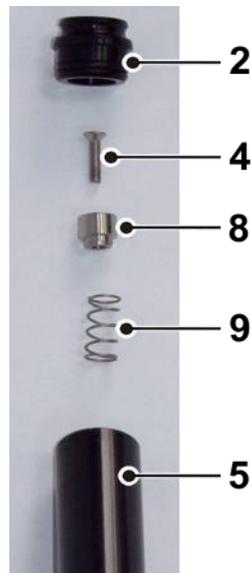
Rotoraufnahme mit Druckstück und Druckfeder
